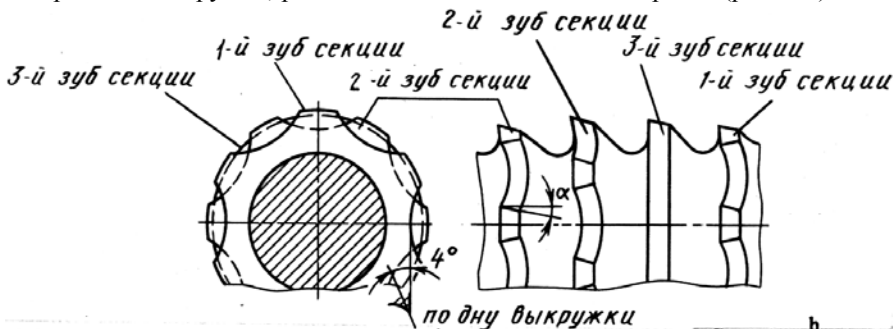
Протяжка круглая с групповой схемой резания
